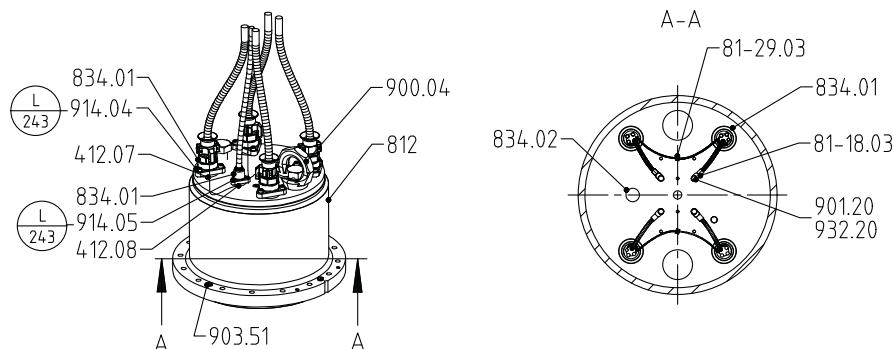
Предварительный монтаж крышки корпуса двигателя
